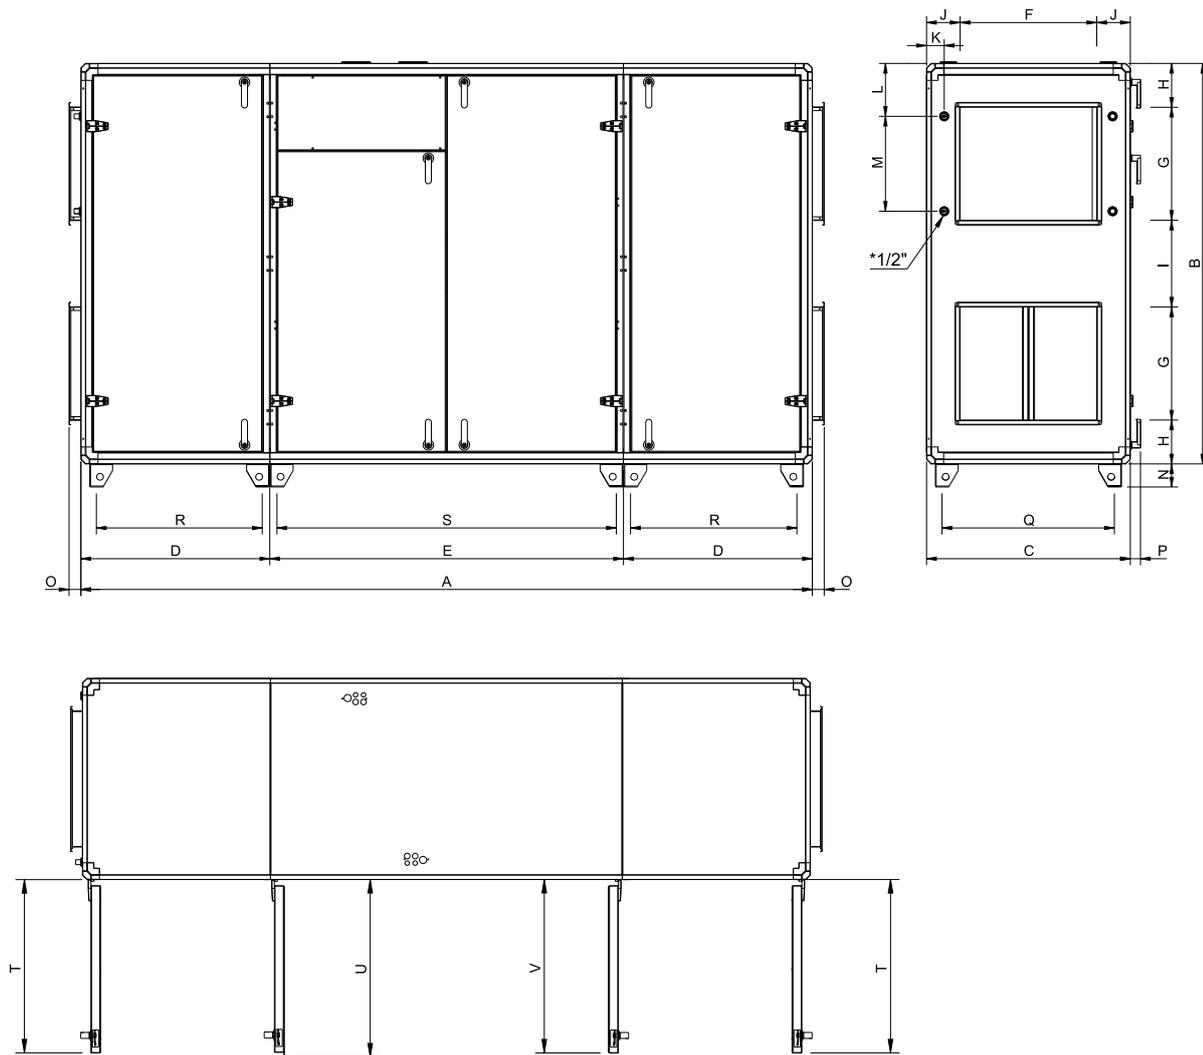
Dimensions (mm) SC06 (version gauche)
